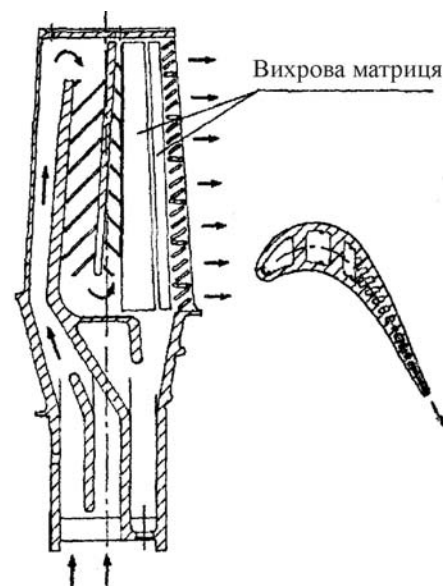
Конструкція охолоджуваної робочої лопатки з вихровою матрицею
